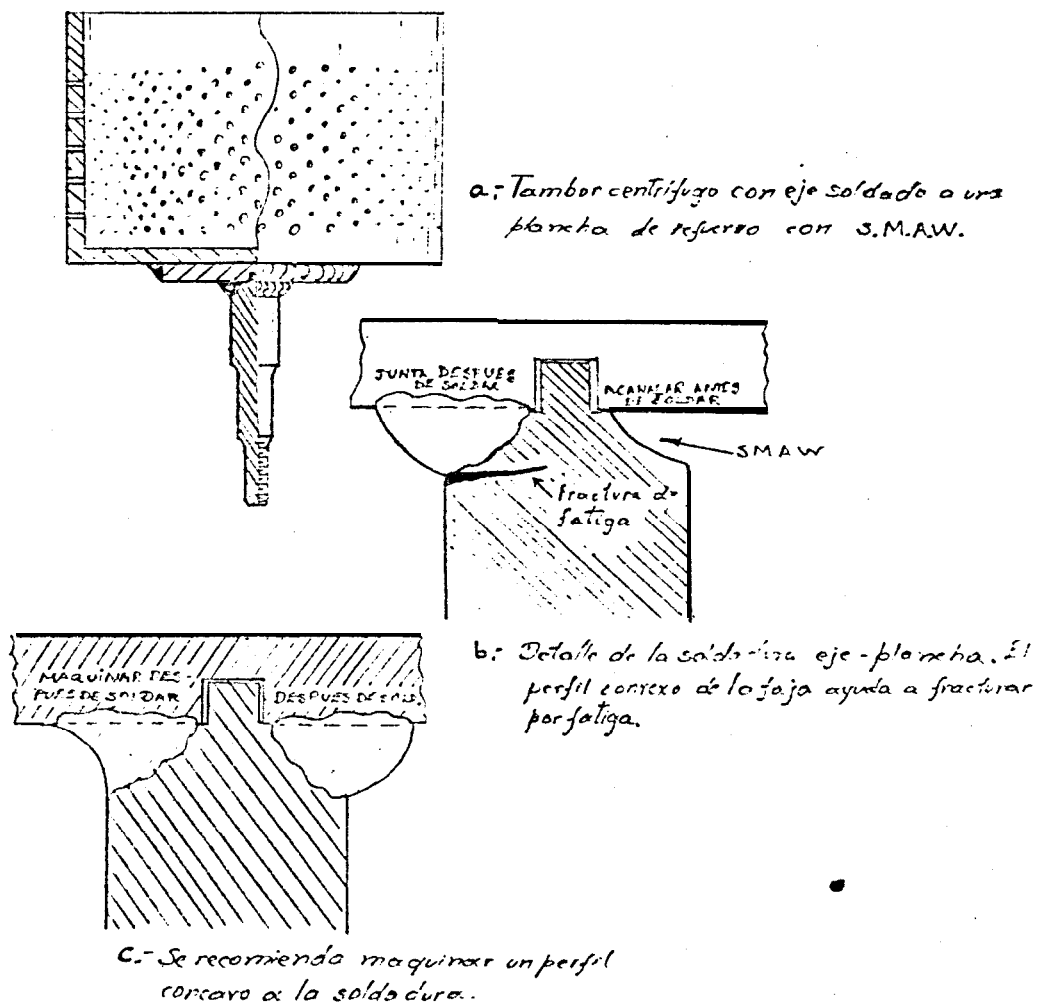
Causa y remedio para fractura de fatiga en el ensamble soldado de un eje y tambor centrífugo.
